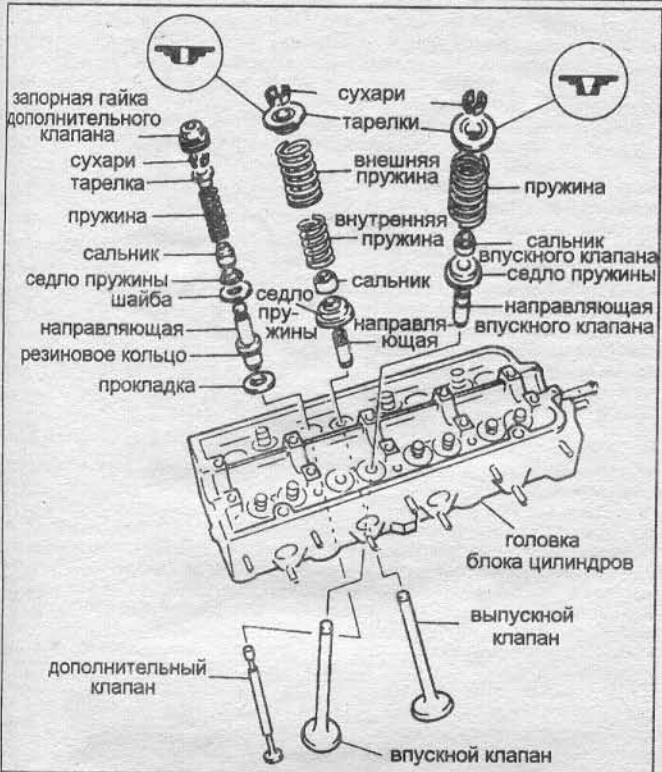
а Головка цилиндров двигателей с дополнительными клапанами (форкамерный).
